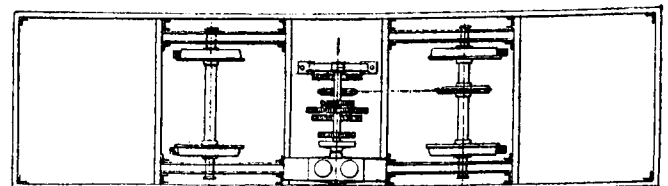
Grundriss in Rahmenhöhe.
